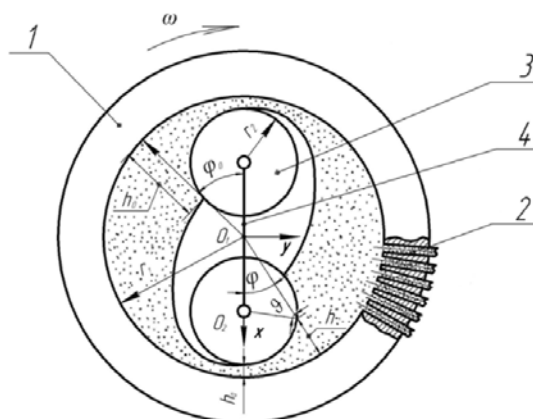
Схема взаємодії оброблюваного матеріалу з робочими органами в пресувальному механізмі з внутрішнім типом контакту: 1 – матриця кільцева; 2 – філь’єра; 3 – ролик пресувальний; 4 – водило механізму пресування
